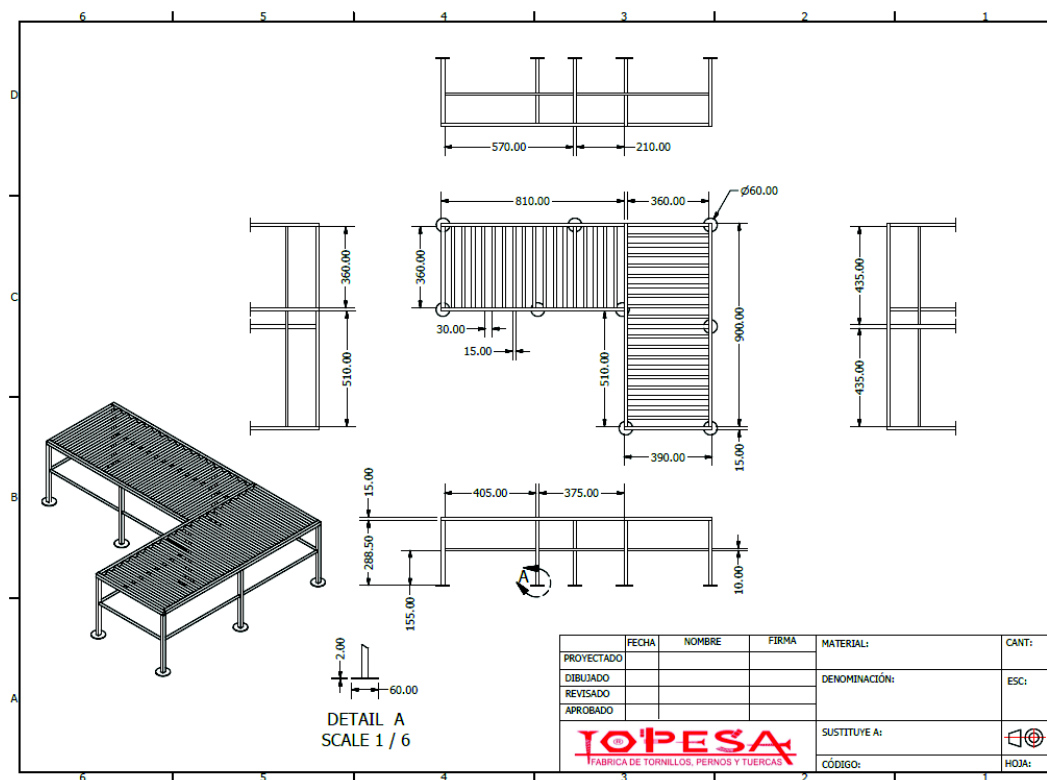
Plano de construcción de la plataforma metálica tipo L, para los puestos de roscado R2 y R3
